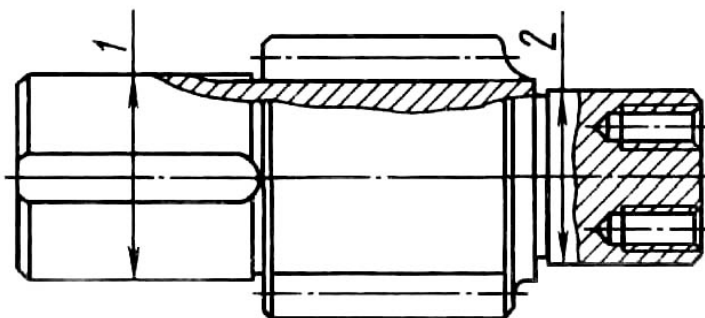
Расположение шеек ведущей цилиндрической шестерни:
